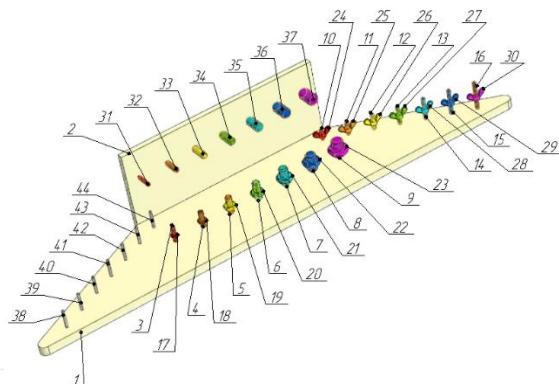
Перспективная модель настольного гаечного тренажёра: 1 – основание; 2 – вертикальная стенка; 3–16 – цилиндрические стержни с правой резьбой; 17–23 – шестигранные гайки, 24–30 – гайки-барашки; 31–37 – цилиндрические стержни с левой резьбой; 38–44 – гладкие стержни
